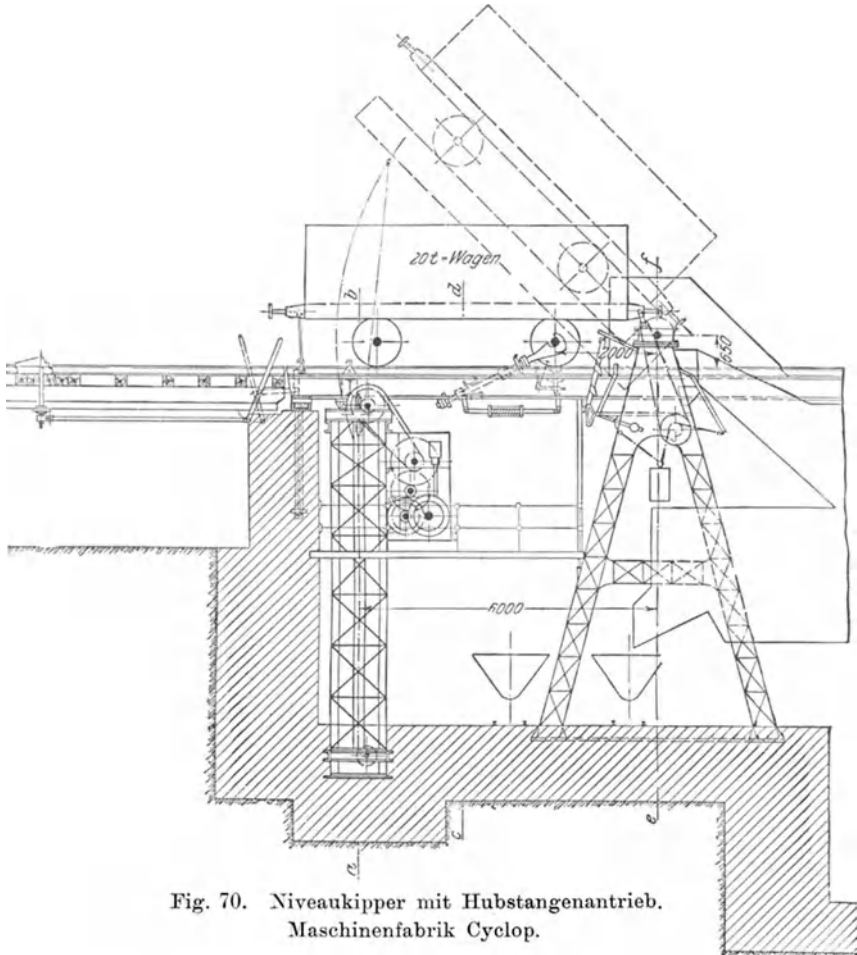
Niveauekipper mit Hubstangenantrieb.
